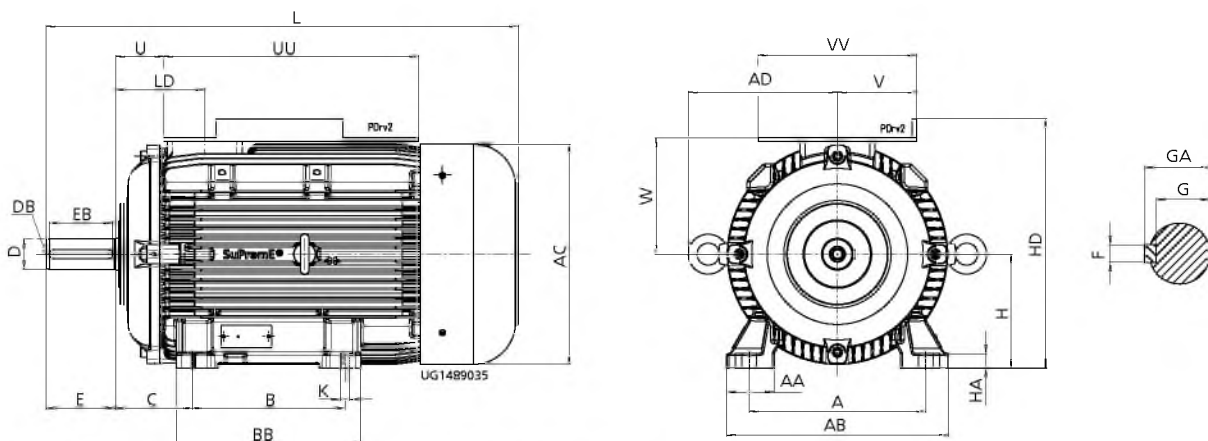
Двигатели с адаптером для PumpDrive 2 со стандартной крышкой подшипников (B3,...)
